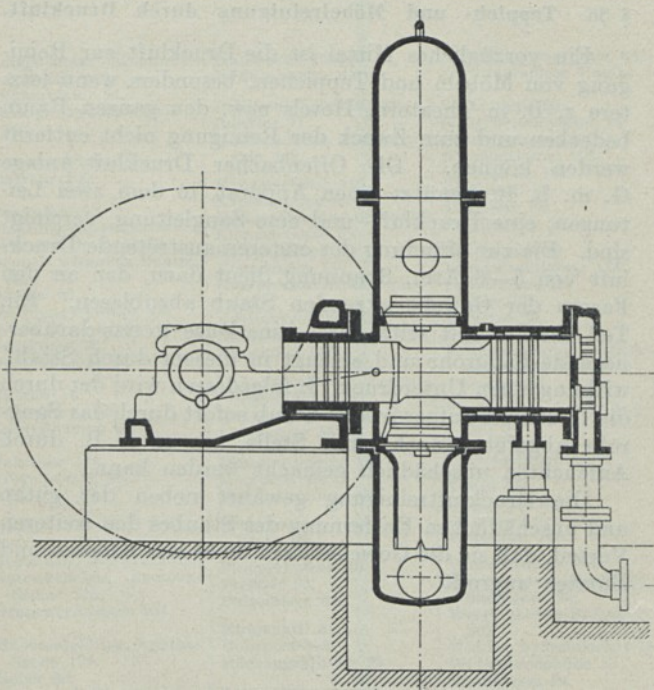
Kompressor-Druckpumpe oder Kreuzpumpe. A. Borsig, Berlin-Tegel.
